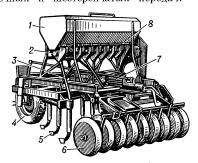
Сеялка-культиватор: 1 — зернотуковый ящик; 2 — высевающий аппарат для зерна; 3 — семяпровод; 4 — опорное колесо передка; 5 — сошник с культиваторной лапой; 6 — прикатывающие катки; 7 — гидроцилиндр; 8 — высевающий аппарат для минеральных удобрений.
